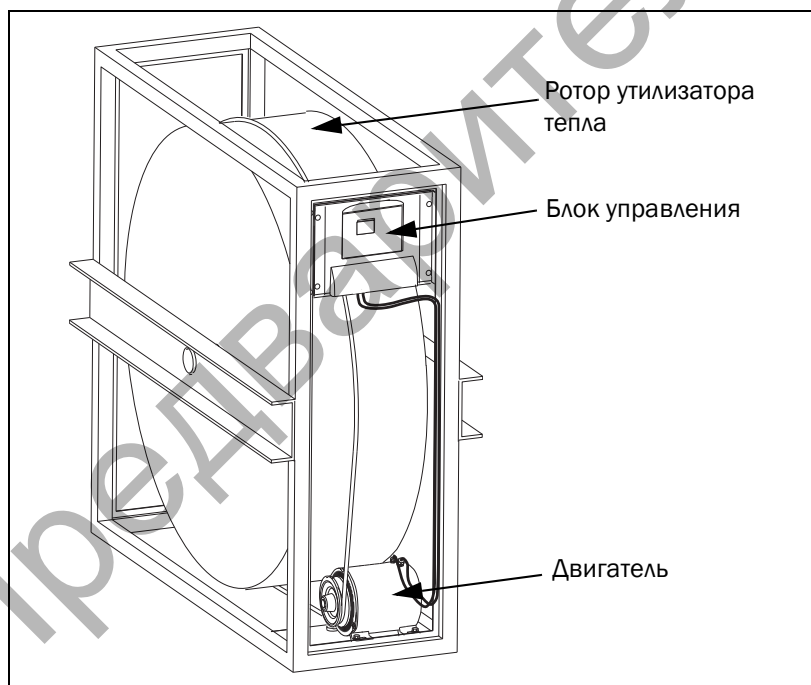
Emotron - двигатель и блок управления для роторного утилизатора тепла
